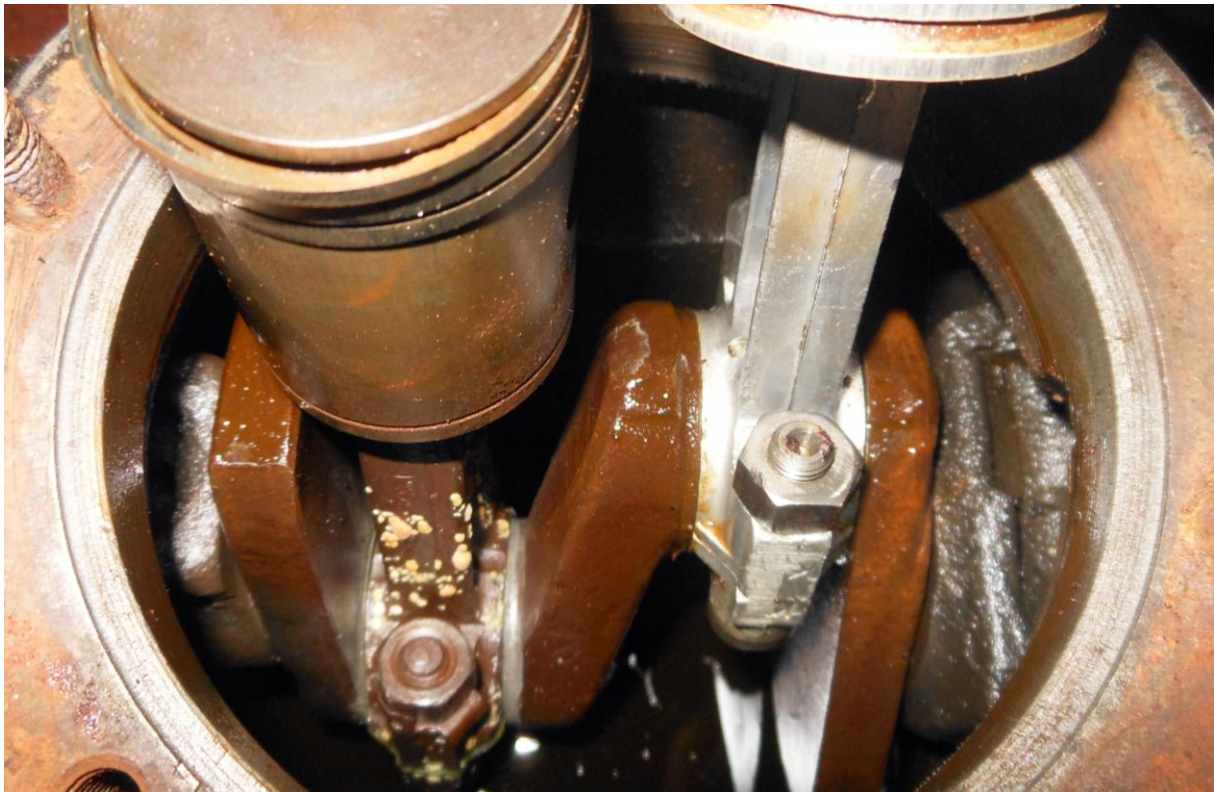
Внешний вид коленчатого вала и его коренных и шатунных подшипников
